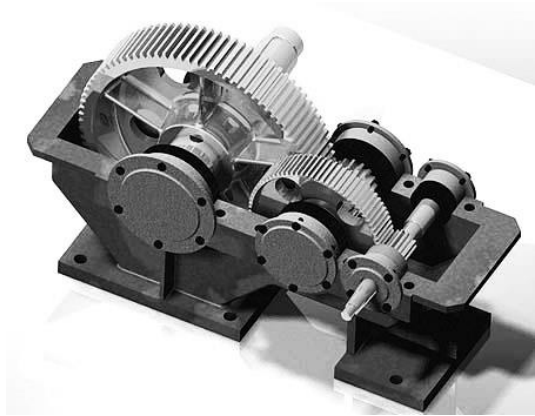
Циліндричний двоступінчастий редуктора за розгорнутою схемою (без кришки)
